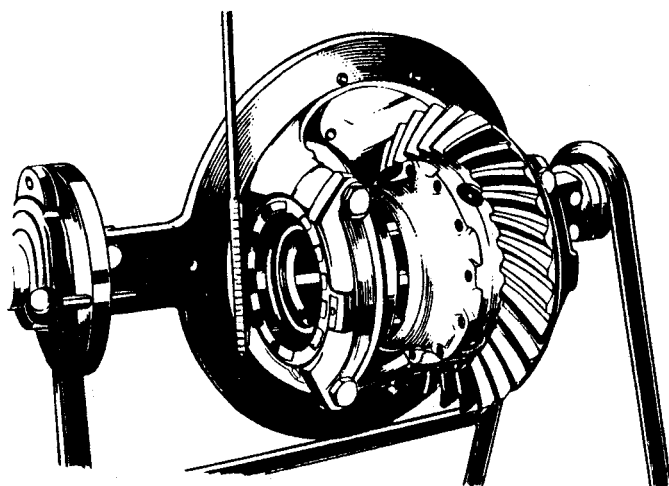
Ключ Т 17 – 393 для опорного кольца подшипника дифференциала
